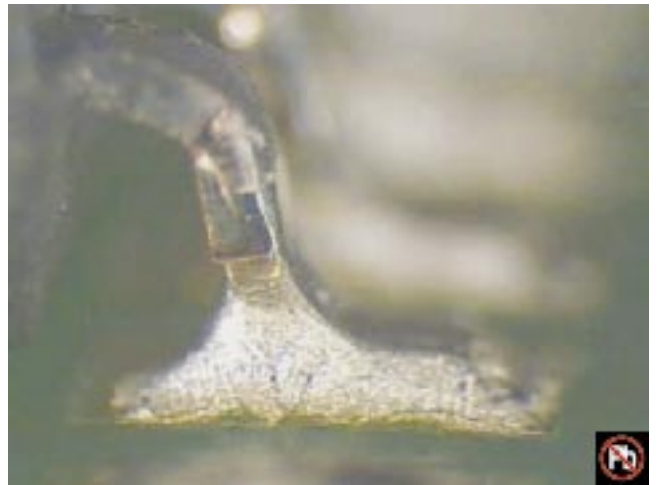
Soldadura SnAgCu; Proceso No-Lavable
